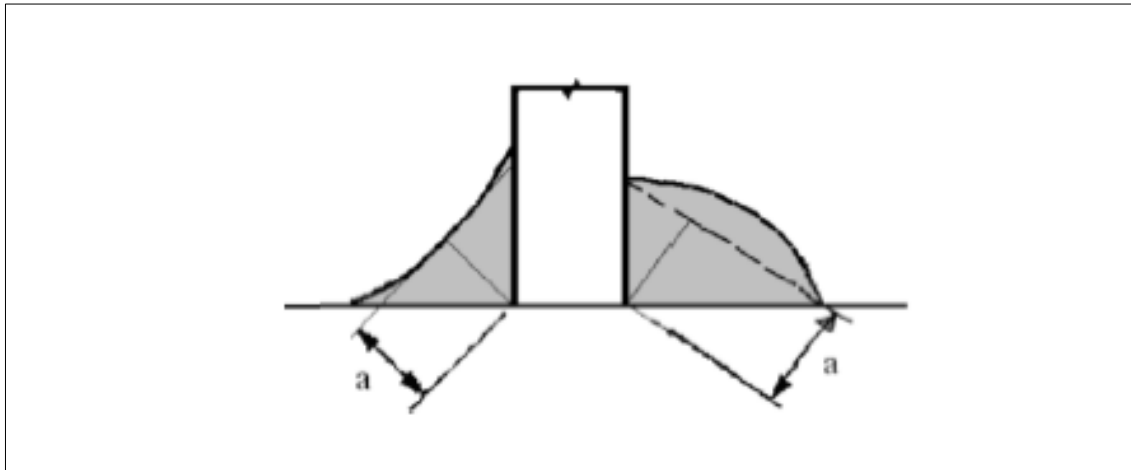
Gorge d'une soudure d'angle.
